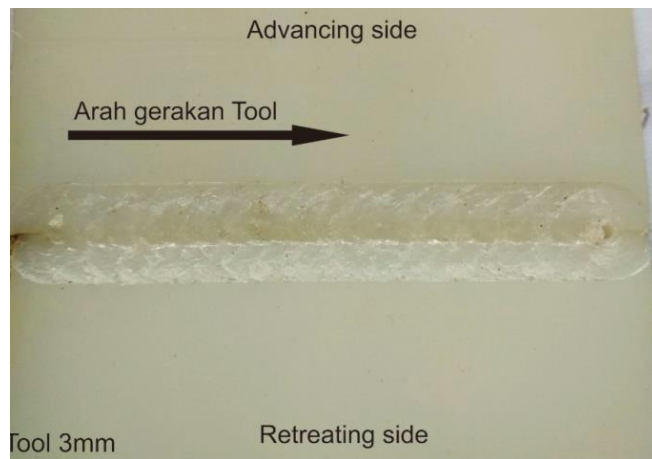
Hasil pengelasan pin silinder 3mm
